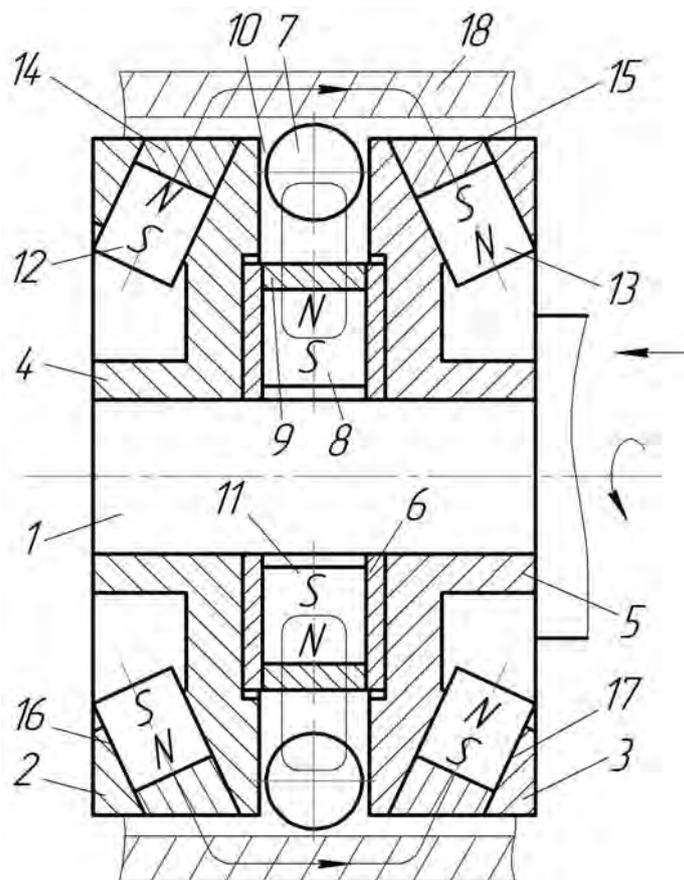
Конструкция инструмента с дополнительной магнитной системой для перемагничивания поверхностного слоя детали
